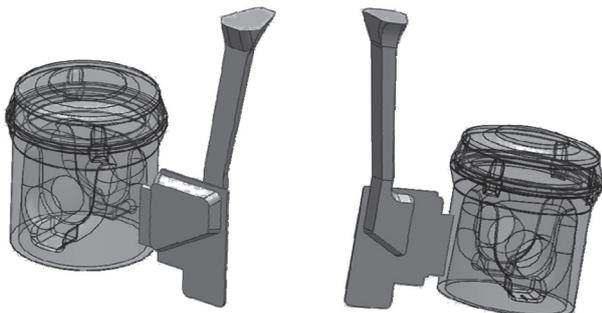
Общий вид литниково-питающей системы для получения отливки «Поршень» (без прибыльной части)
